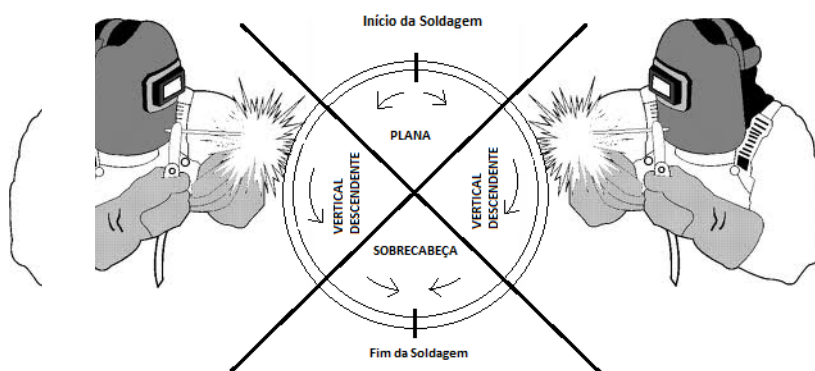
Soldagem durante a fase de construção de dutos utilizando dois soldadores simultaneamente.
